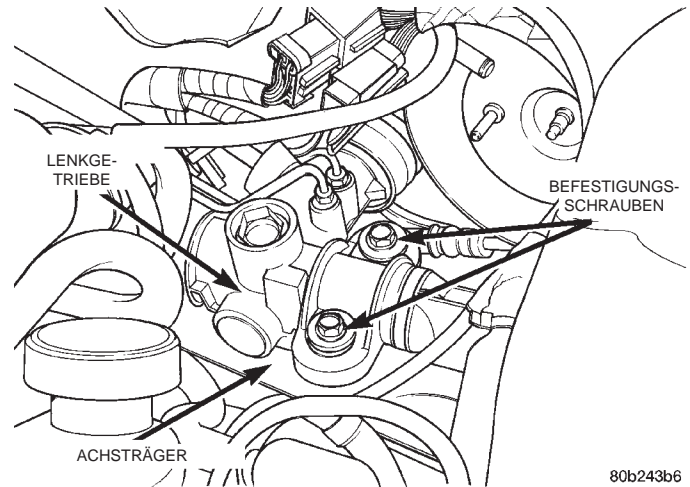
Befestigung des Lenkgetriebes am Achsträger (linke Seite)
